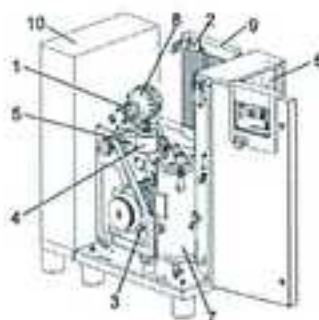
Конструкция компрессора: 1 – впускной клапан; 2 – обратный клапан минимального давления; 3 – двигатель компрессора; 4 – масляный фильтр; 5 – компрессорный блок; 6 – распределительный шкаф; 7 – маслоотделитель; 8 – воздушный фильтр; 9 – масляный и воздушный радиатор; 10 – шкаф для холодоосушителя
